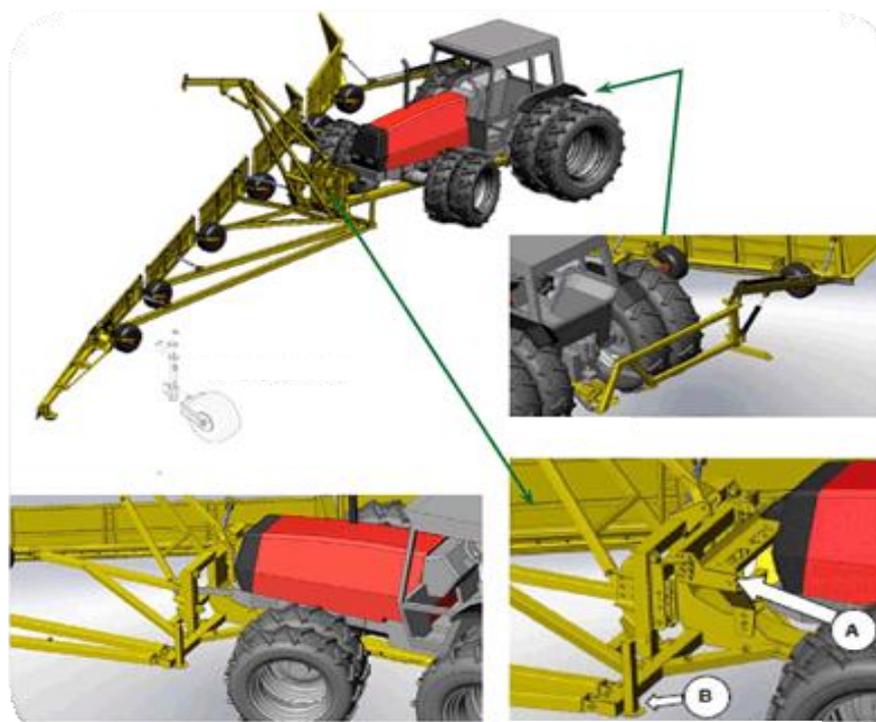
Грядоделитель фрезерного торфа JVK-9HPN
